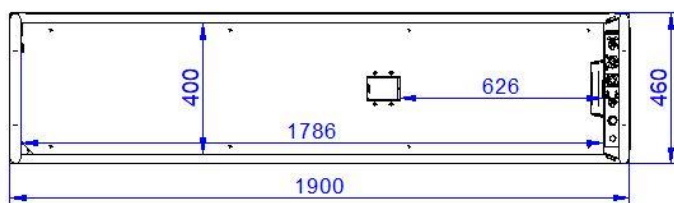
; Dimensions de la plateforme en mm, 3 pantographes
